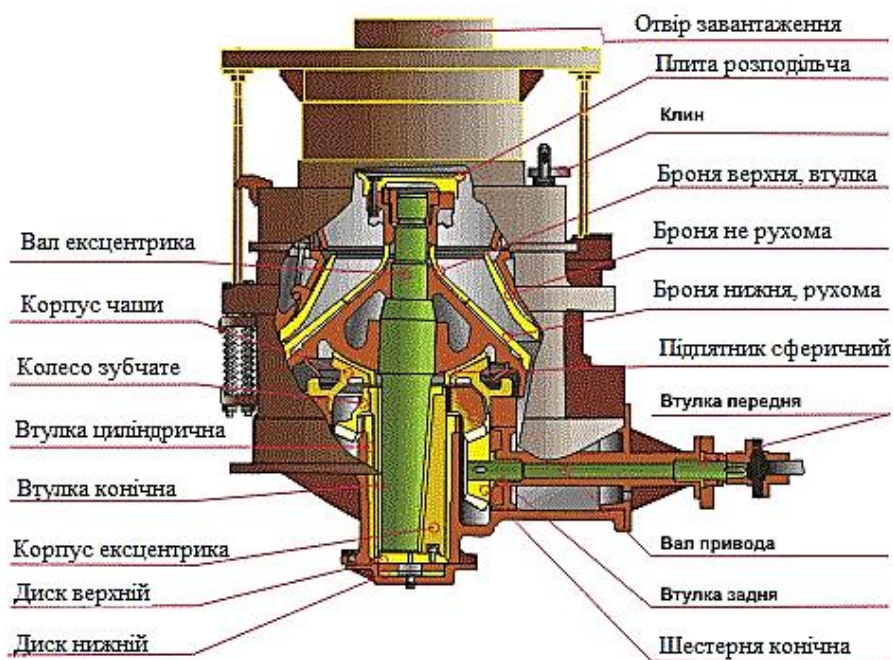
Конструкція конусної дробарки середнього дроблення (КСД2200Т)
